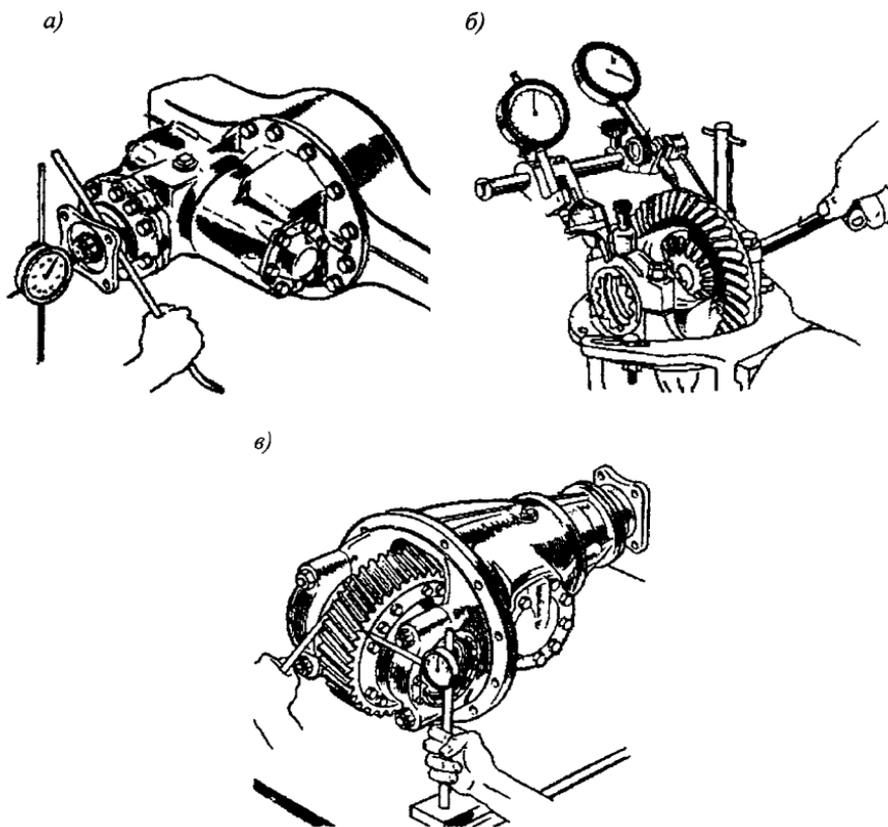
Определение зазора в подшипниковых узлах главной передачи:
